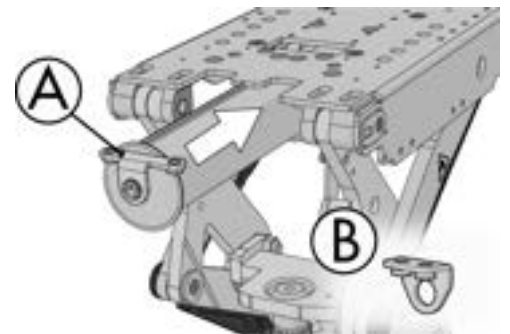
Drücken Sie das Kunststofflager auf die Spindel.
